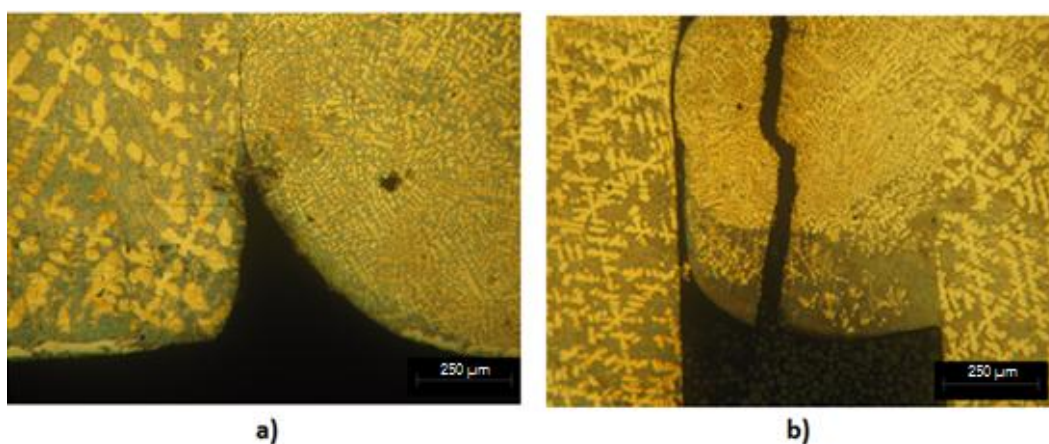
Fusão incompleta dos ensaios de teste, soldados a 110 A e com pré-aquecimento de 250 °C: a) amostra 1 arrefecida ao ar; b) amostra 2 arrefecida no forno a partir de 250 °C.
